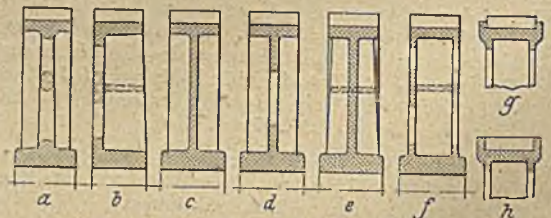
Querschnitte durch die gebräuchlichsten Stirnradformen.
